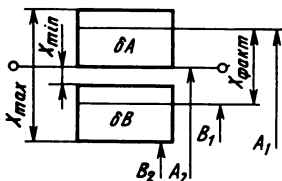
Стандартное расположение полей допусков при методе подбора
